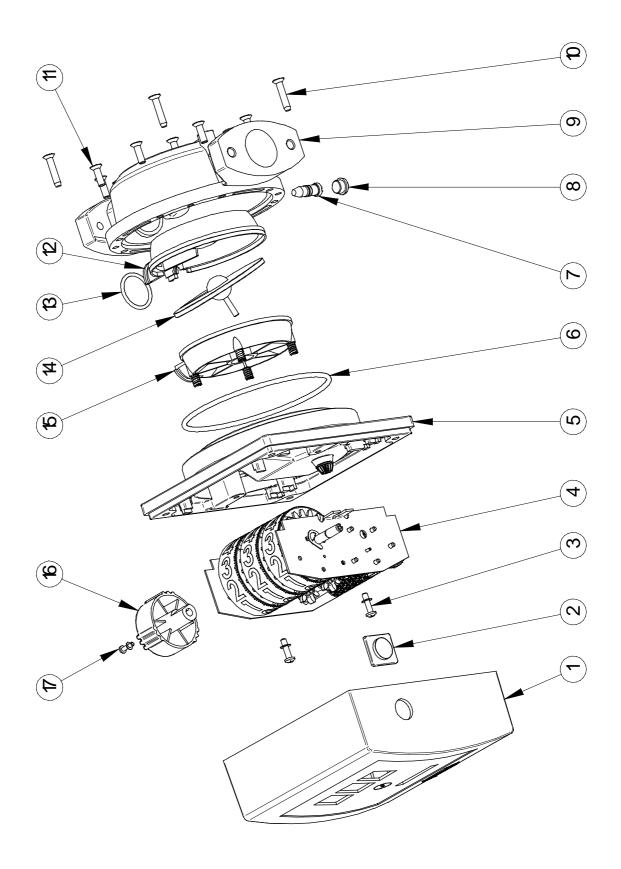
Desenho de explosão do contador de disco oscilante
